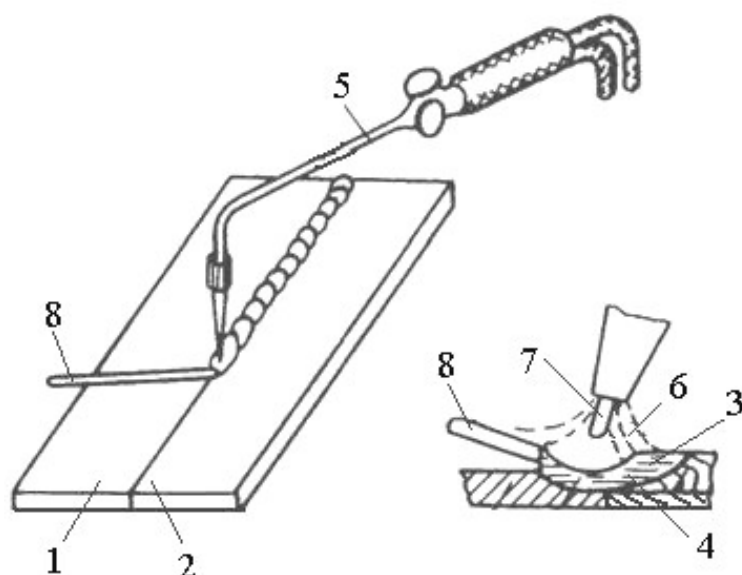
Схема газовой сварки: 1, 2 – свариваемые детали; 3 – ванна жидкого металла; 4 – металл твердого шва; 5 – горелка; 6 – ацетилено-кислородное пламя; 7 – ядро пламени; 8 – присадочный пруток
